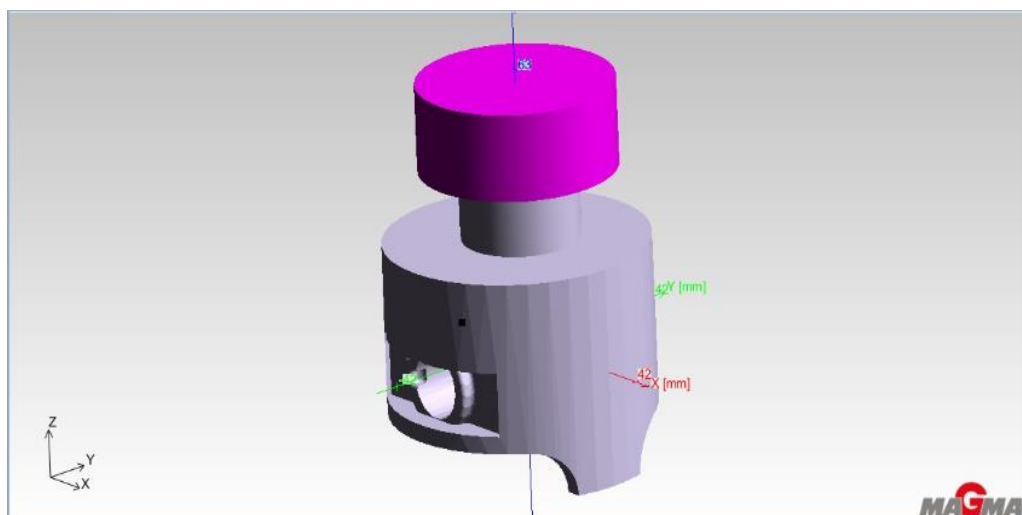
Ensamblaje de los componentes del sistema de colado de la fundición
